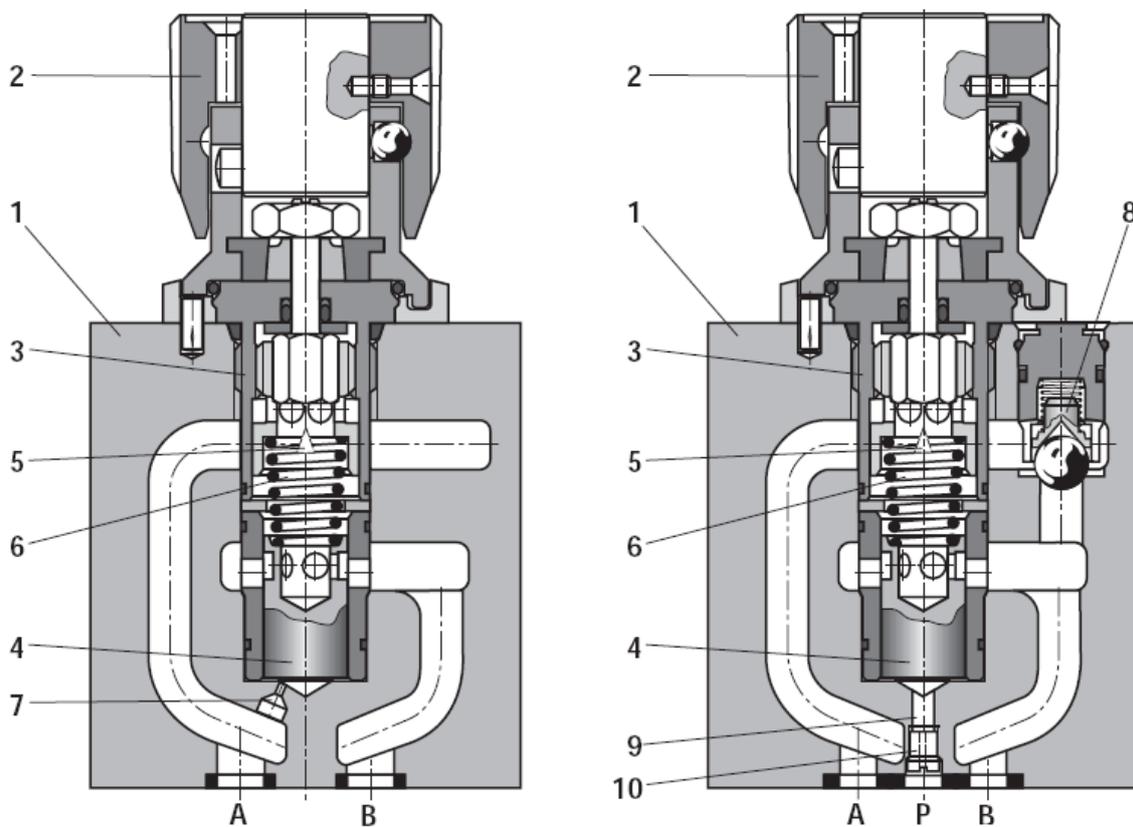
Конструкция регуляторов расхода с монтажом на плите
